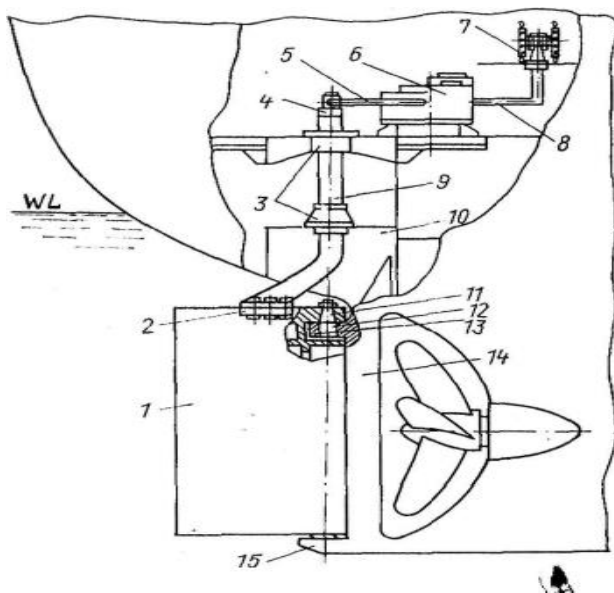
Схема рулевого устройства морского транспортного судна: 1 – перо руля; 2 – фланцевое соединение пера руля и баллера; 3 – опоры баллера; 4 – голова баллера; 5 – рулевой привод; 6 – рулевая машина; 7 – штурвал ручного управления; 8 – рулевая передача; 9 – баллер; 10 – гельмпортная труба; 11 – петля пера руля; 12 – штырь; 13 – петля рудерпоста; 14 – рудерпост; 15 – пятка ахтерштевня
